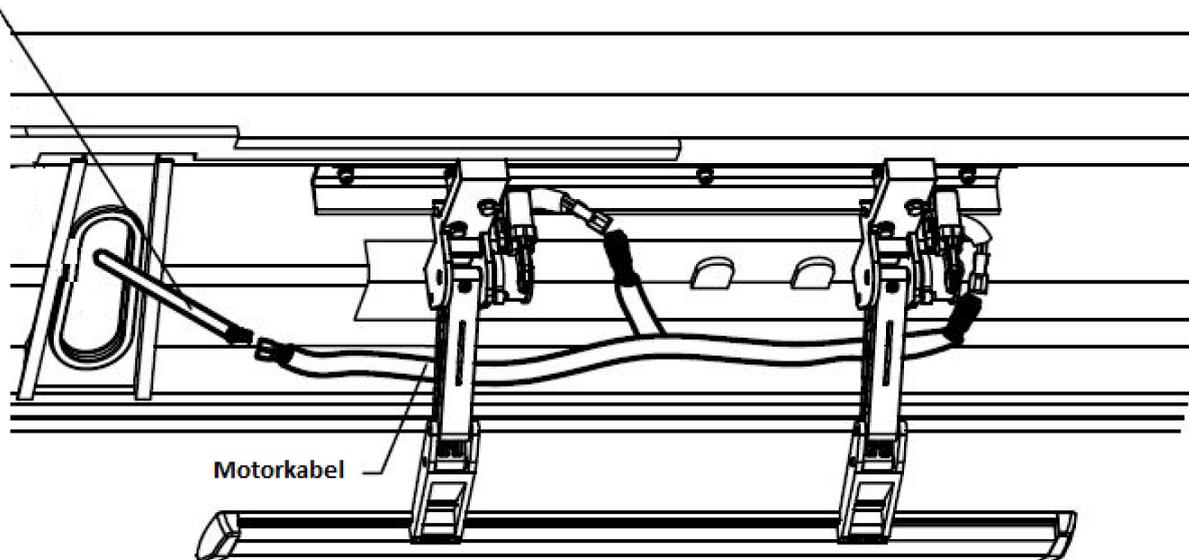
Steckverbindung Motorkabel Innen-Außen
